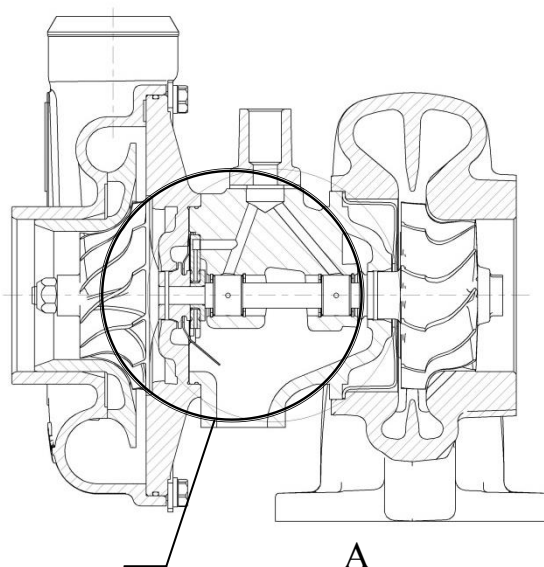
Схема установки для проверки герметичности подшипникового узла с ротором турбокомпрессора.
